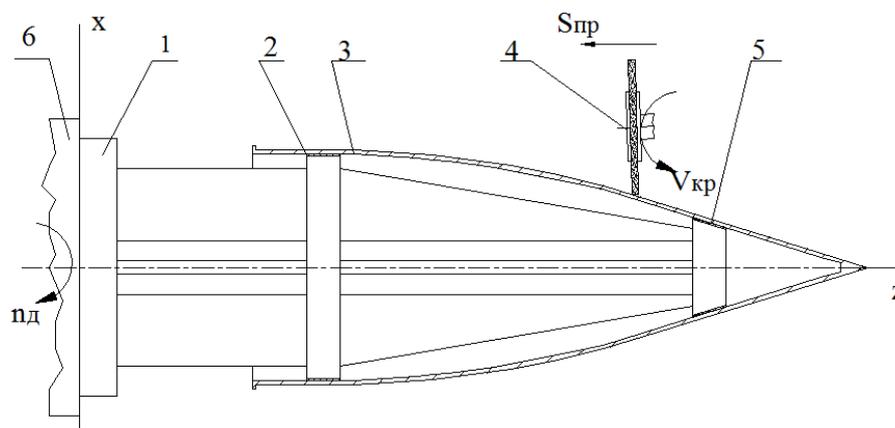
Схема технологической системы при наружном круглом шлифовании детали – тонкостенной оболочки вращения из ситалла: 1 – оправка; 2, 5 – втулки из гетинакса (элементы приспособления – оправки); 3 – обрабатываемая деталь; 4 – шлифовальный круг IAI 200x10x3x76 AI – 315/250-4- M2-01, установленный в агрегатной головке; 6 – шпиндель станка
